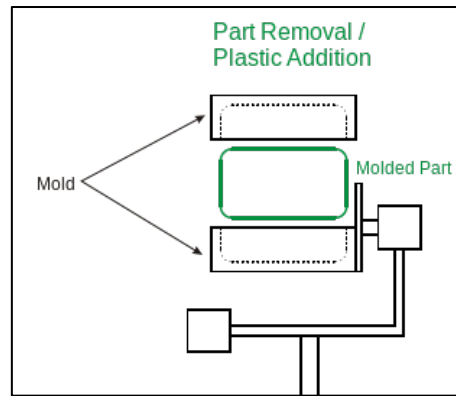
Fase de desmoldeo y obtención del producto terminado. FUENTE: [6]
